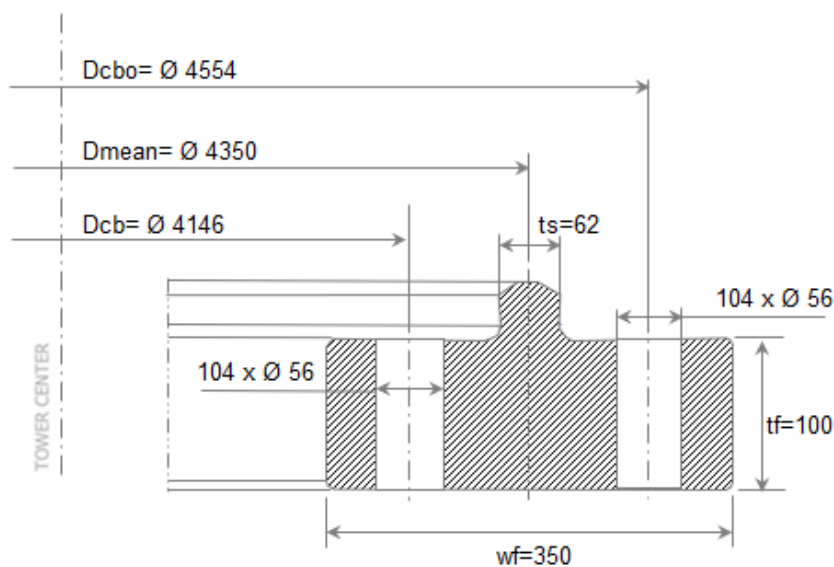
Dimensioni della flangia a T inferiore della torre SG 6.6-170 T115-58B
